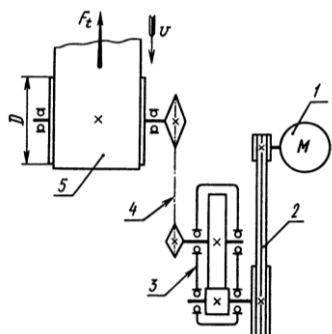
Схема привода ленточного транспортера: 1 – электродвигатель; 2 – ременная передача; 3 – редуктор цилиндрический одноступенчатый; 4 – цепная передача; 5 – ленточный транспортер
